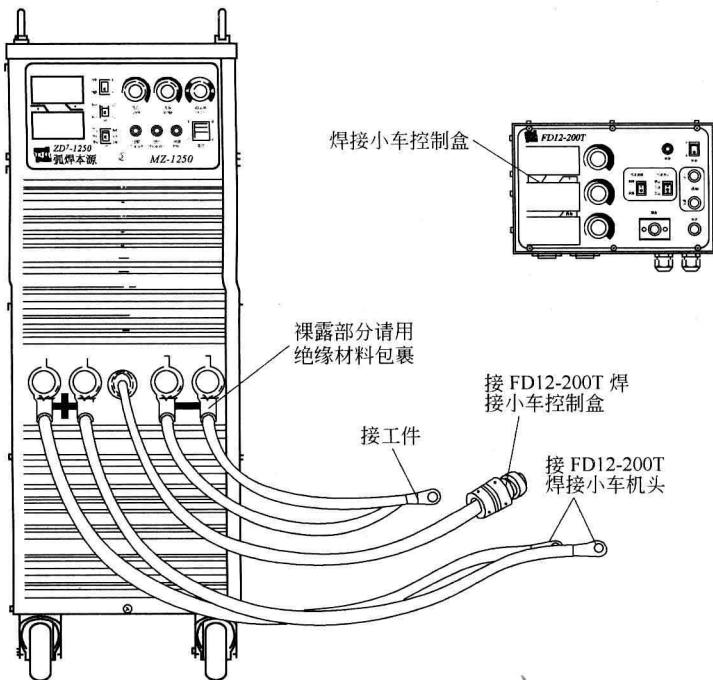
MZ-1000 型埋弧焊外部接线图（直流）
